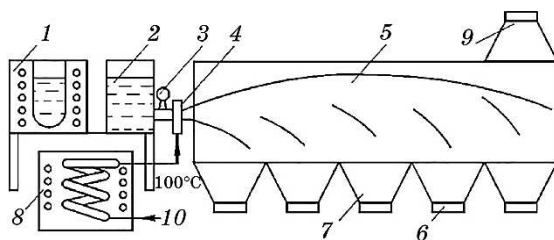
Установка для получения порошка с индукционным плавлением металла и распылением расплава газом: 1 — печь; 2 — металлоприёмник; 3 — вентиль; 4 — форсунка; 5 — камера распыления; 6 — затвор; 7 — бункер; 8 — печь для подогрева воздуха; 9 — выход воздуха; 10 — подача воздуха.⁸
